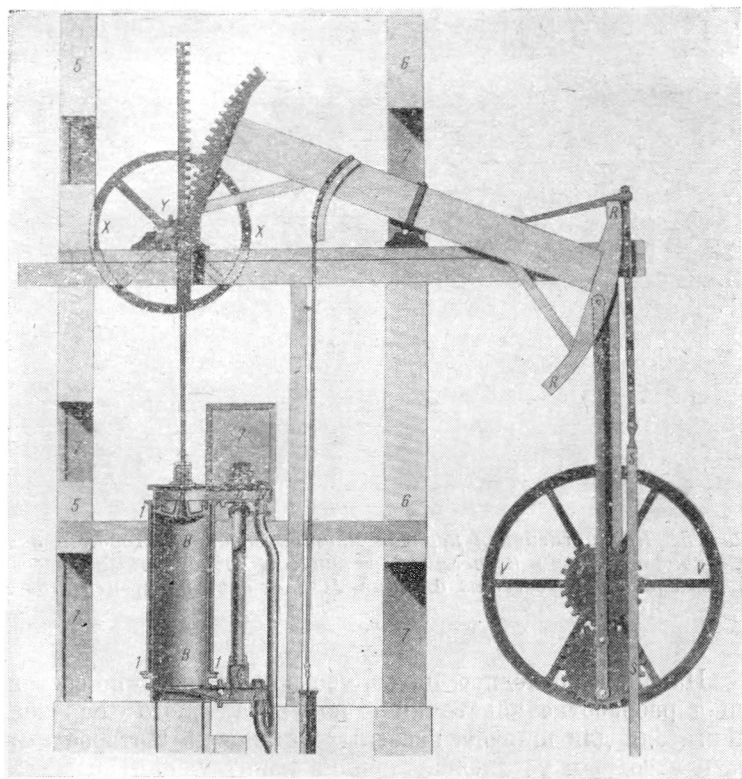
Универсальный паровой двигатель двойного действия с зубчатой рейкой и планетарным соединением шатуна с валом машины. Приложение к патенту 1782 г.
